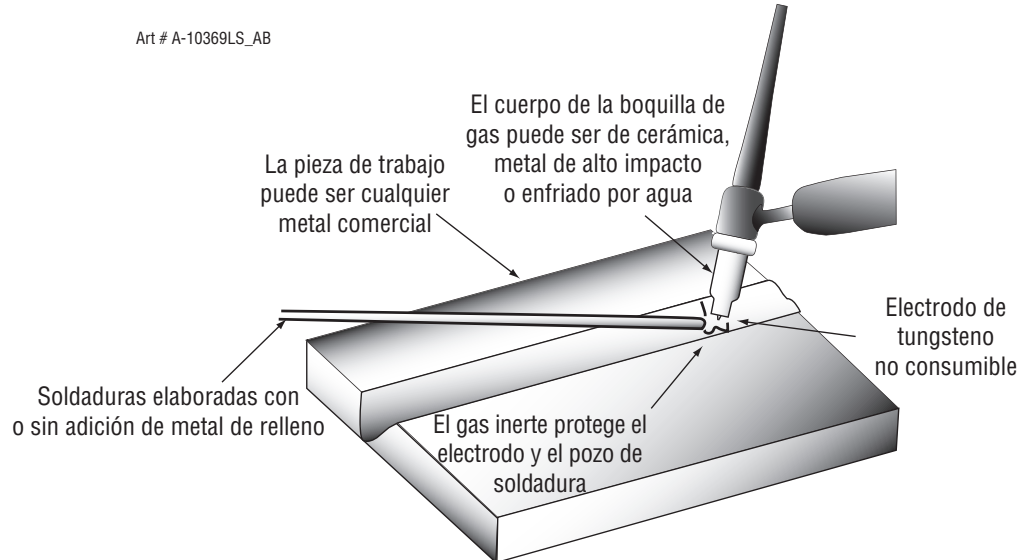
Esquema de la aplicación de la soldadura TIG (GTAW)
